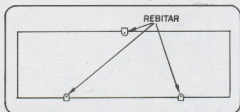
Detalhe da colocação das três plaquetas de metal.
